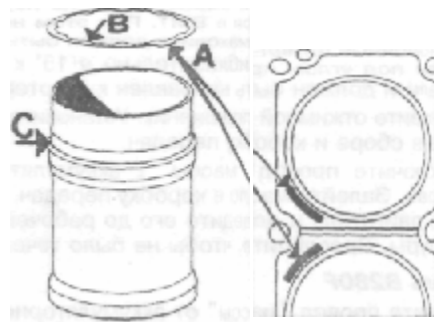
Правильное расположение кольца гильзы цилиндра — Двигатель B280F
